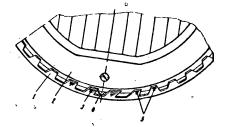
Расположение фиксатора-выступа сбодка насадки и прямых зубьев отражателя: -отражатель; 2—насадка к фаре; 3—прямые зубцы отражателя; 4—фяксатор-выступ ободка насадки; 5—скошенные зубцы отражателя
